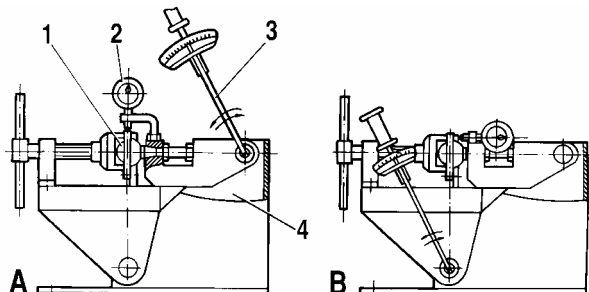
Проверка шарового шарнира на приспособлении 02.8701.9502:
